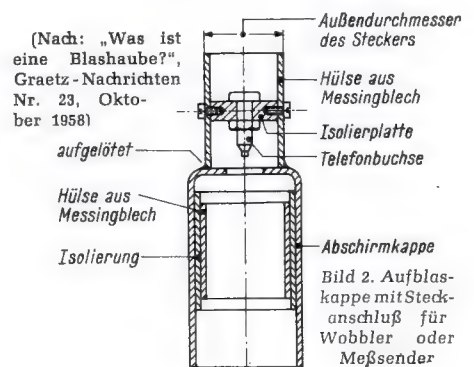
Aufblaskappe mit Steckanschluß für Wobler oder Meßsender
